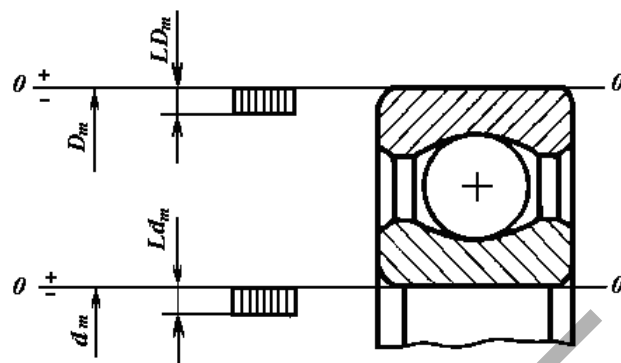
Расположение полей допусков подшипников
